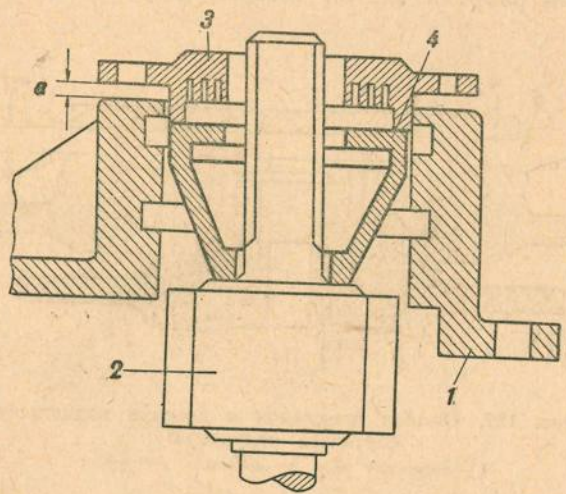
Подбор прокладок под фланец крышки маслоотражателя ведущего вала
